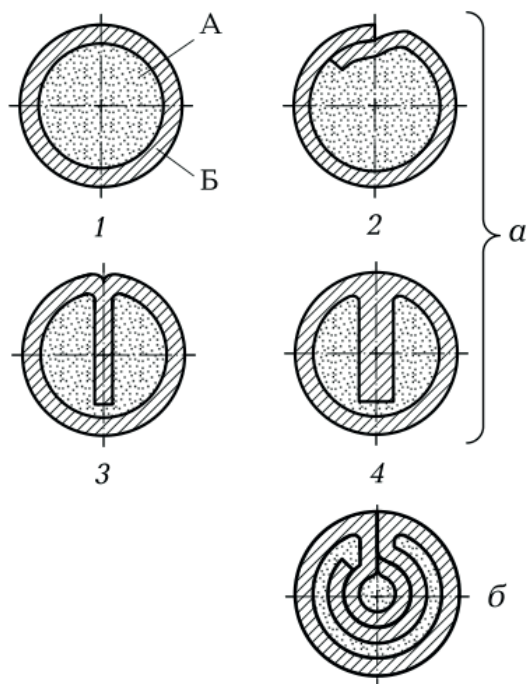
Конструкції порошкового дроту: *а* – одношарова (1 – трубчаста; 2 – з нахлестом; 3, 4 – із загином оболонки); *б* – двошарова; А – порошкова серцевина; Б – сталева оболонка
